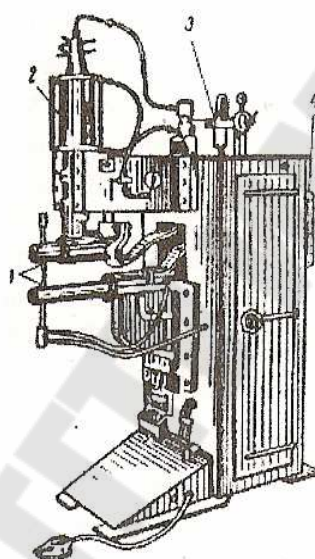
Машина точечной сварки МТ-ІС10: 1 – электроды, 2 – пневмоцилиндр, 3 – лубрикатор, 4 – регулятор времени
